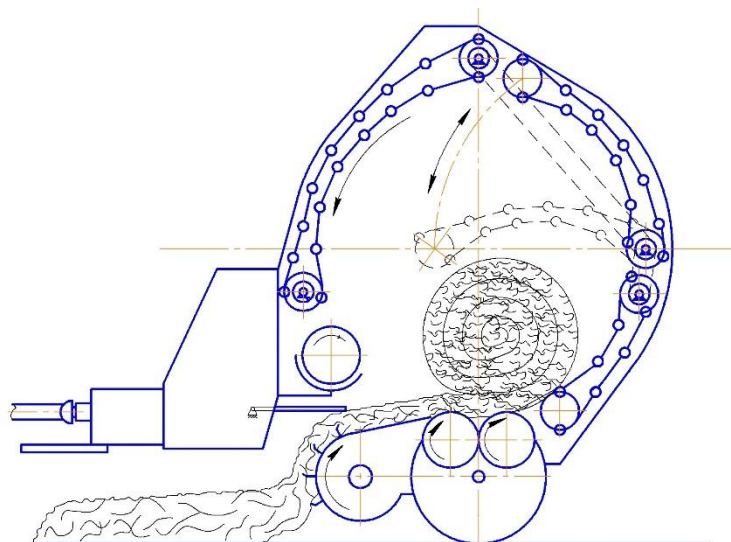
Схема модернизированного пресс-подборщика с цепочно-роликовым прессовальным контуром
